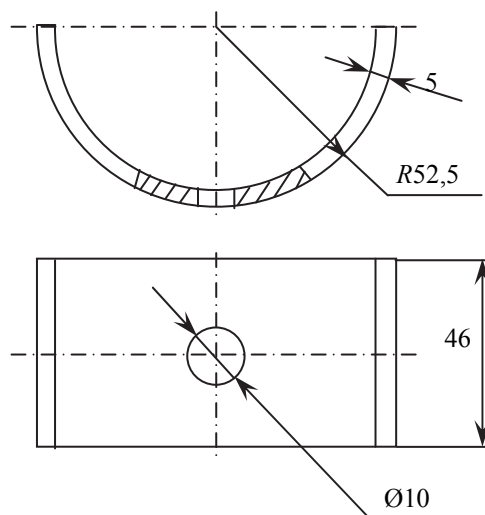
Схема и геометрические размеры конструктивно подобного образца
